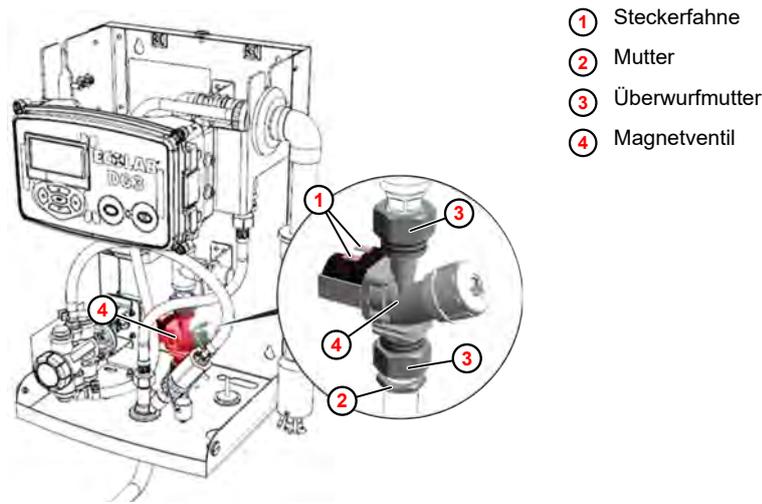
Magnetventil ausbauen (Beispiel DG3)
